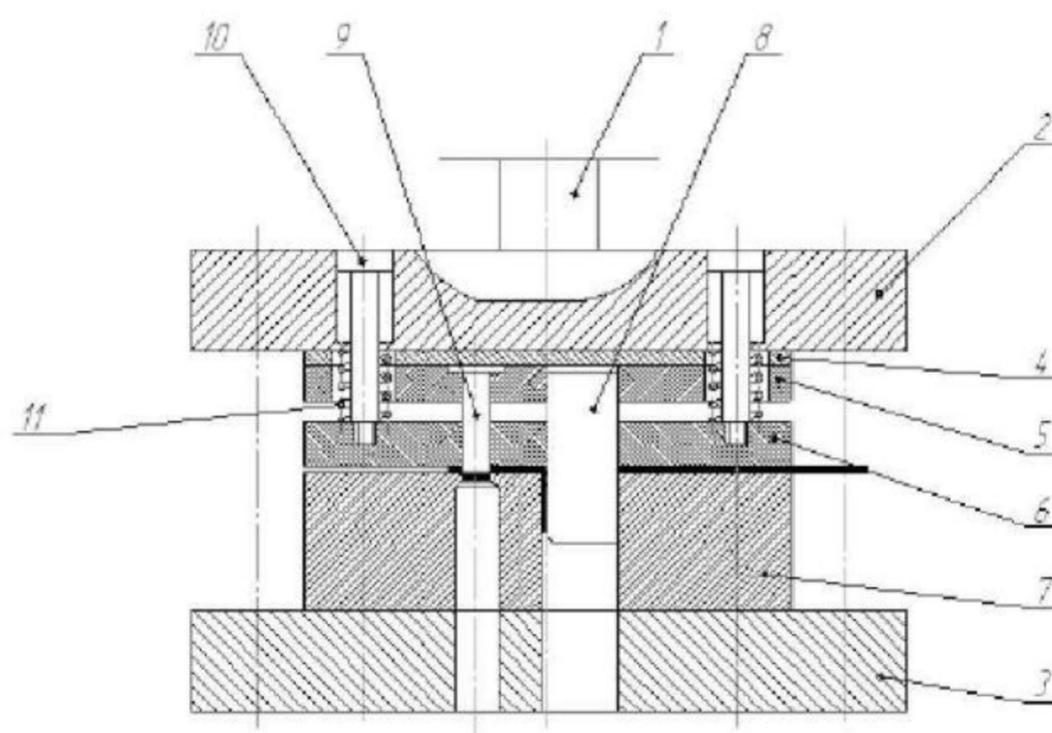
Схема штампа совмещённого действия для пробивки, отрезки и гибки
